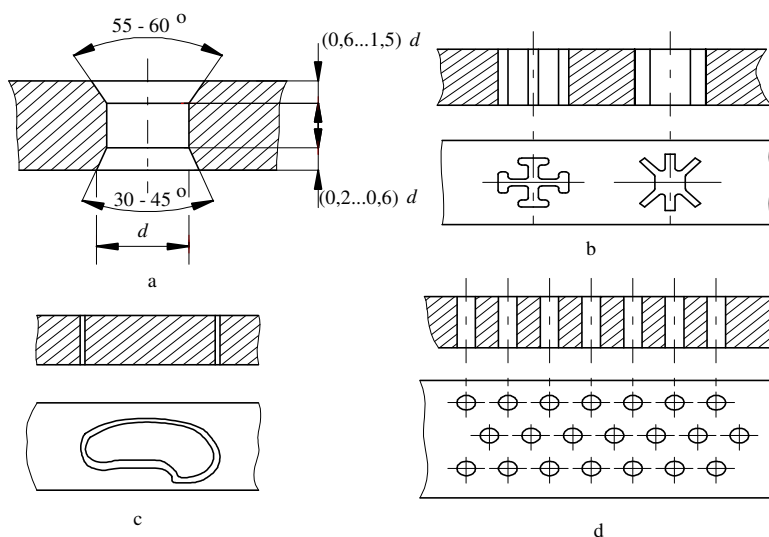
Exemple de operații de prelucrare dimensională cu fascicul de electroni:
